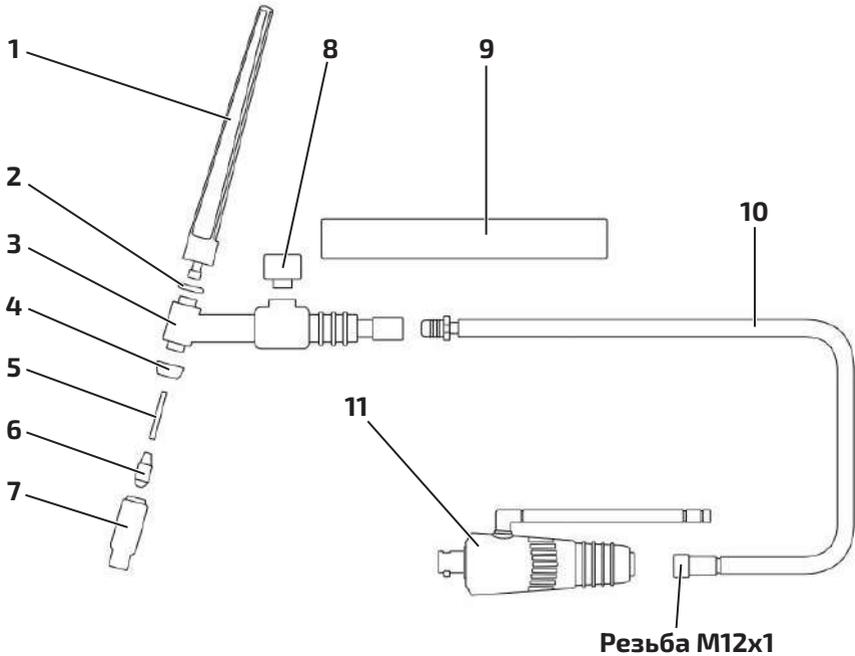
Схема вентильной горелки для аргонодуговой сварки.
